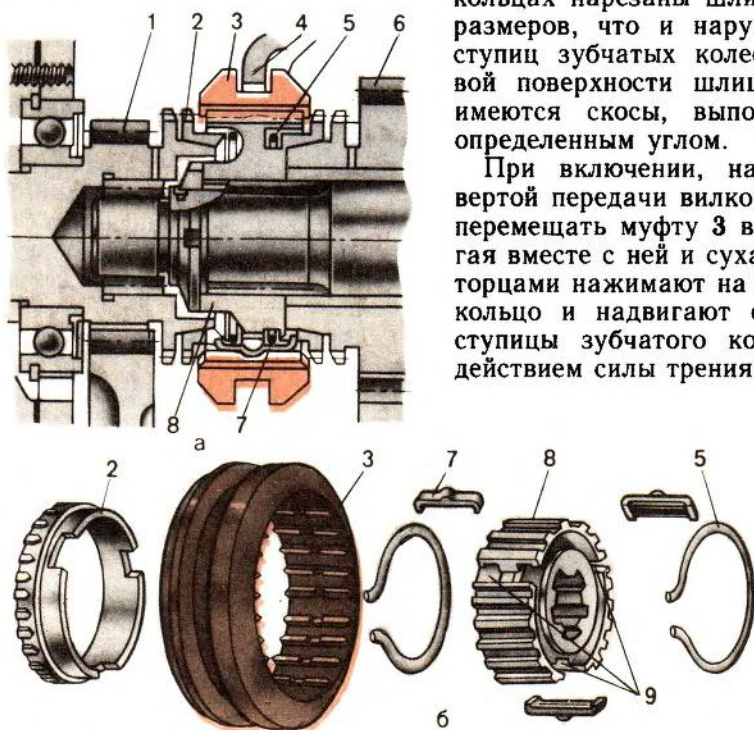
Синхронизатор (а) коробки передач автомобиля ГАЗ-53-12 и его детали (б):
